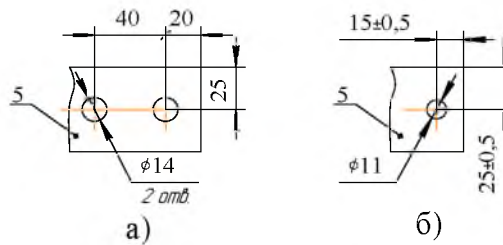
Контактный вывод разъединителя со стороны неподвижной колонки:
